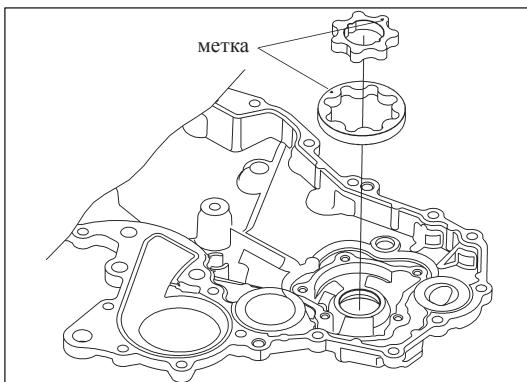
Установка ведущей и ведомой шестерен
